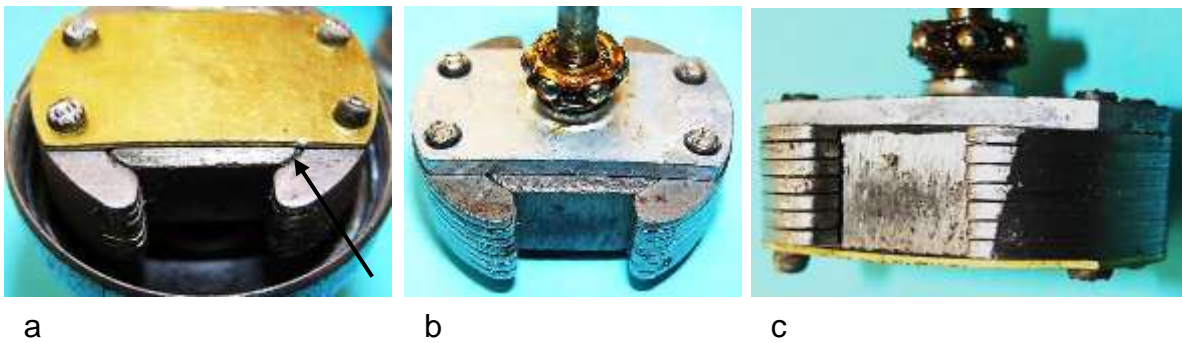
Polrad: a) Unteres Stirnblech, b) Wellenposition auf dem oberen Stirnblech, c), Magnetabmessungen: 24,5 mm x 10 mm x 20 mm, 7 Polradbleche mit 1,5 mm Dicke
